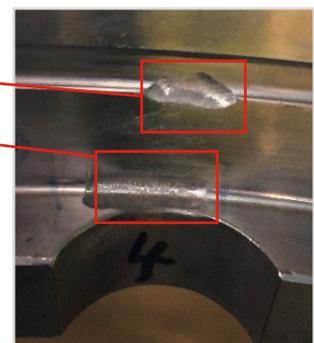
Beseitigung des Fehlers und Schweißen
